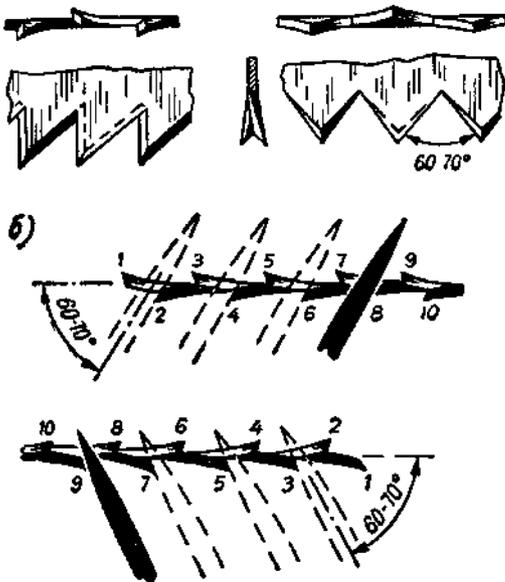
Заточка зубьев поперечной пилы; а — форма зуба; б — схема заточки.
